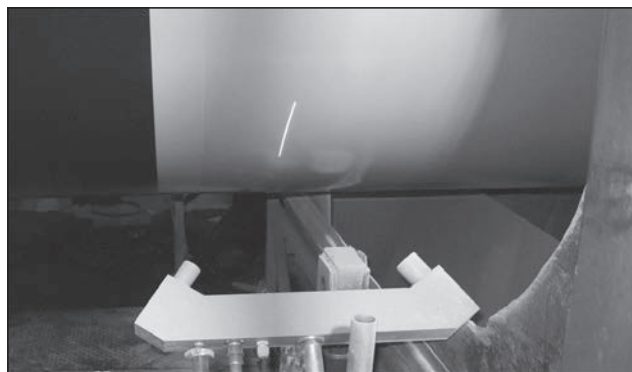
Сканирование поверхности вращающейся трубы лазерным датчиком системы обнаружения сварного шва SFS-P08
